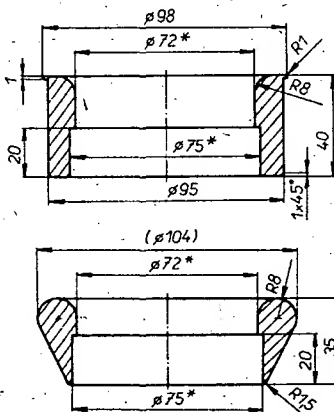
Tubus pro uchycení reproduktoru ARN 8604 v tandemu
